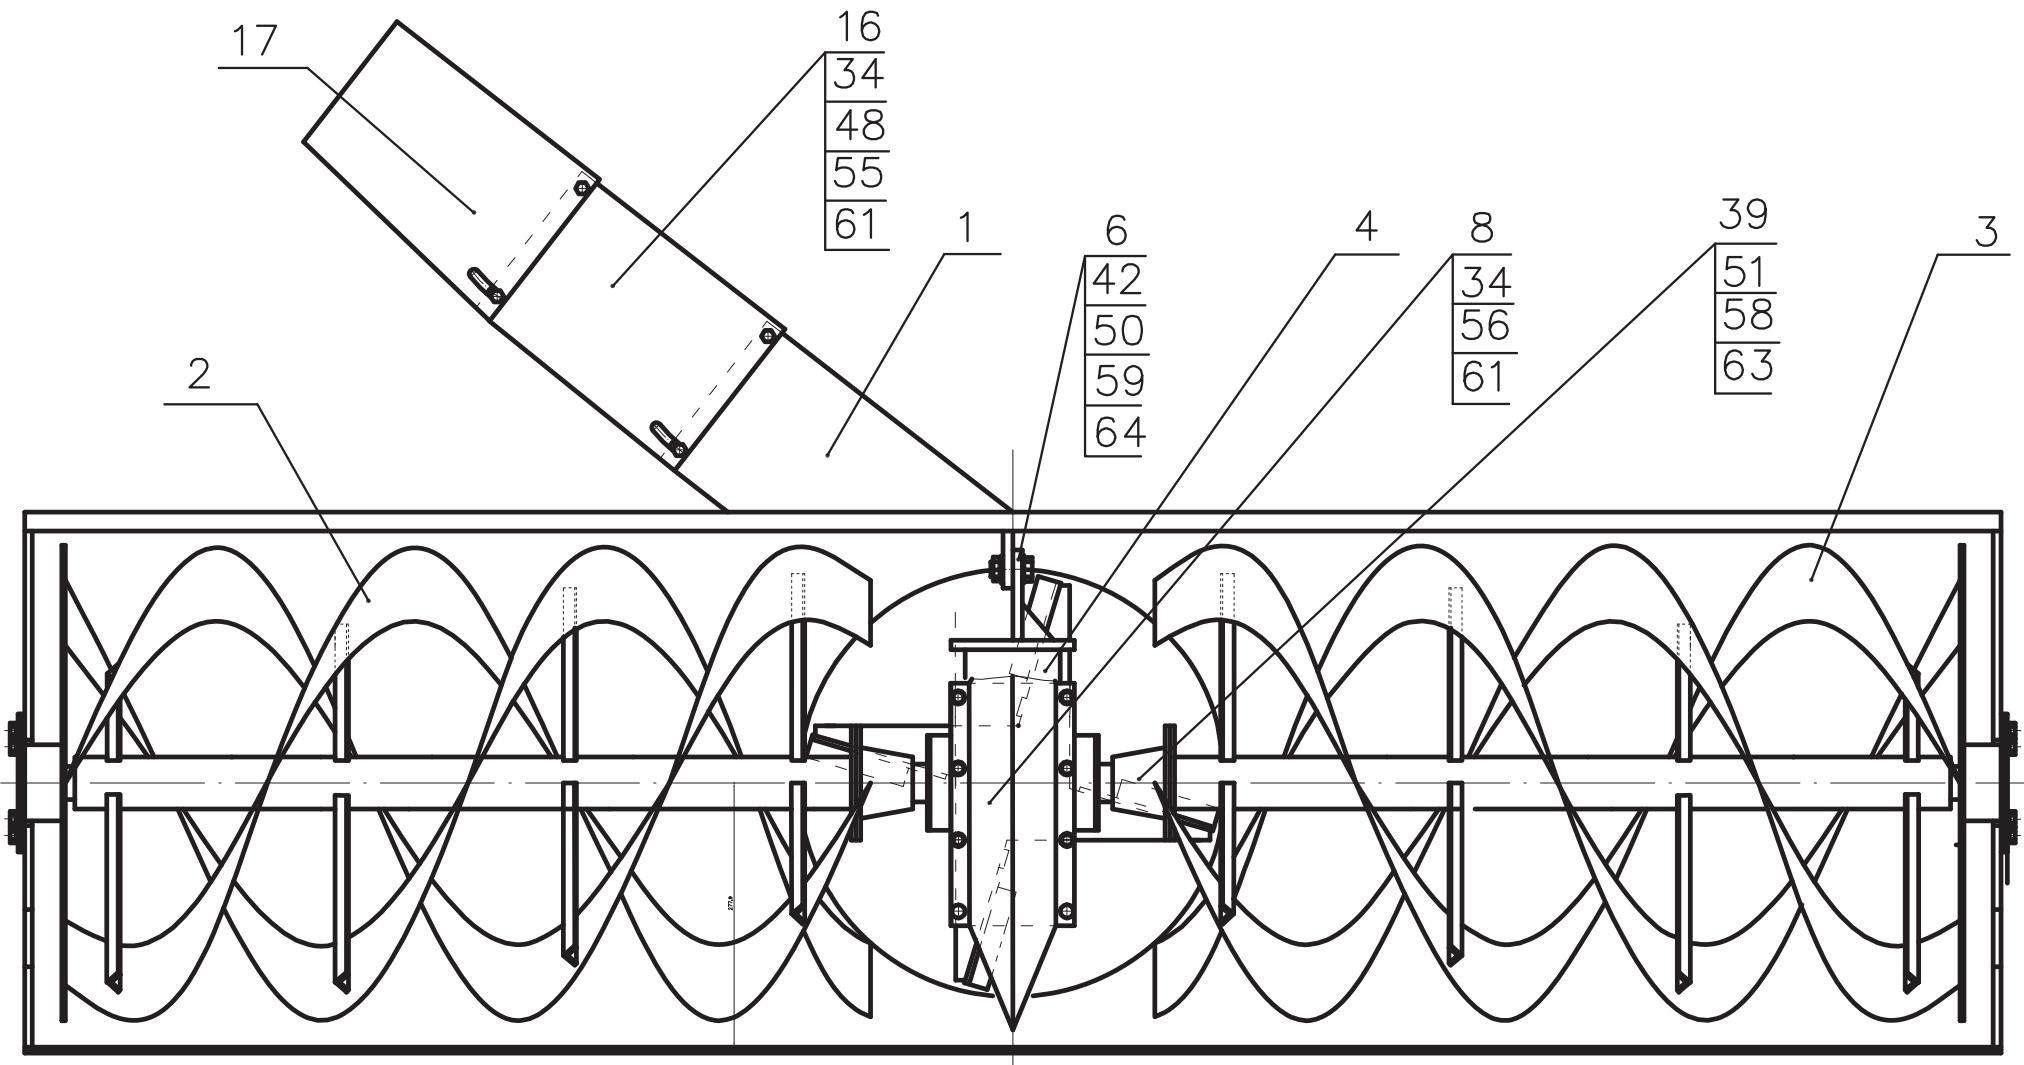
208.46.55.000	Снегоочиститель фрезерно-роторный
